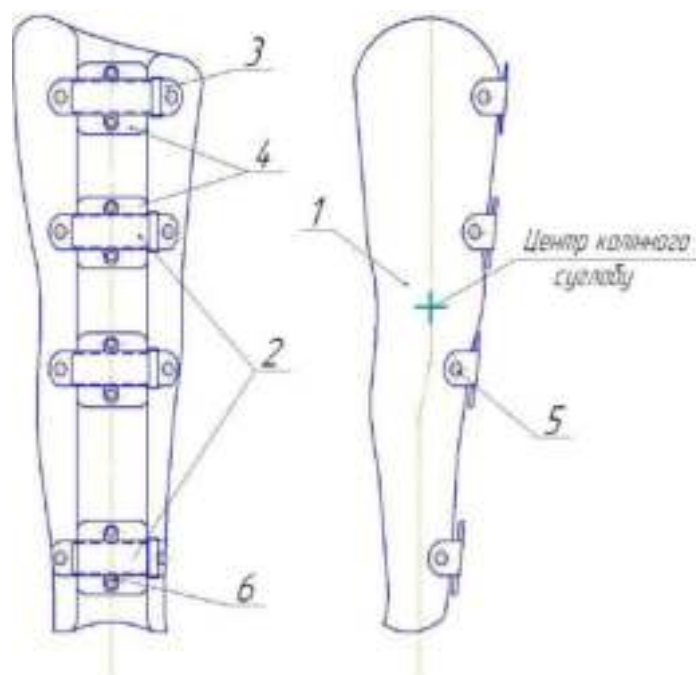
Загальний вигляд безшарнірного ортеза на колінний суглоб:
